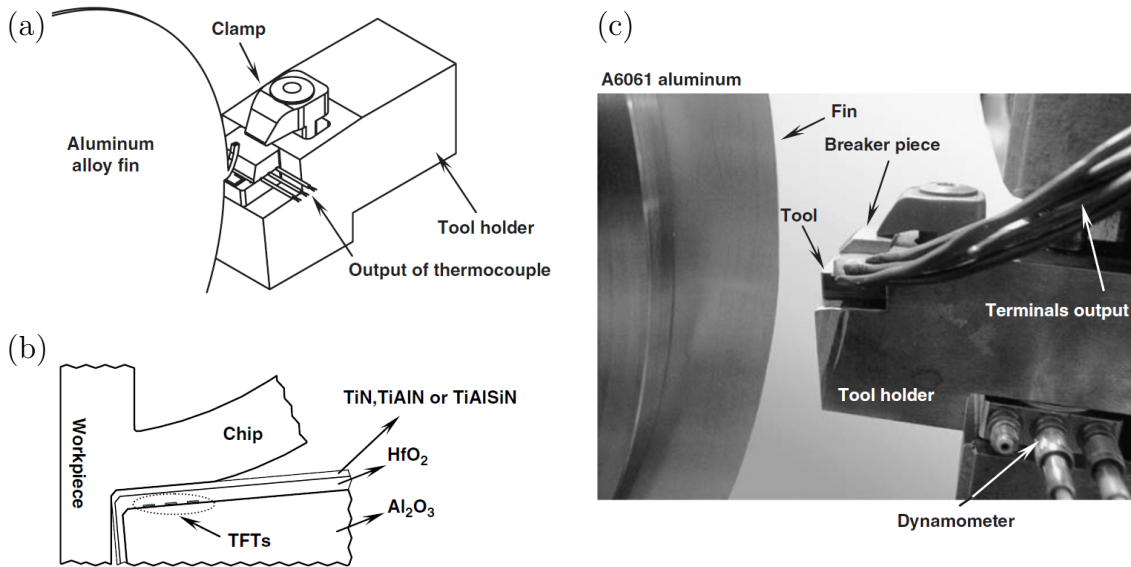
(a) Aufbau einer Werkzeugaufnahme in einer Drehbank für Werkzeuge mit integrierten Dünnschicht-Thermokontakten (*TFT*). (b) Schnittbild durch das Werkzeug im Zerspanungsprozess (schematisch, Schichtdicken nicht maßstabsgetreu). (c) Fotografie eines eingebauten und kontaktierten Werkzeugs. Aus [73].
